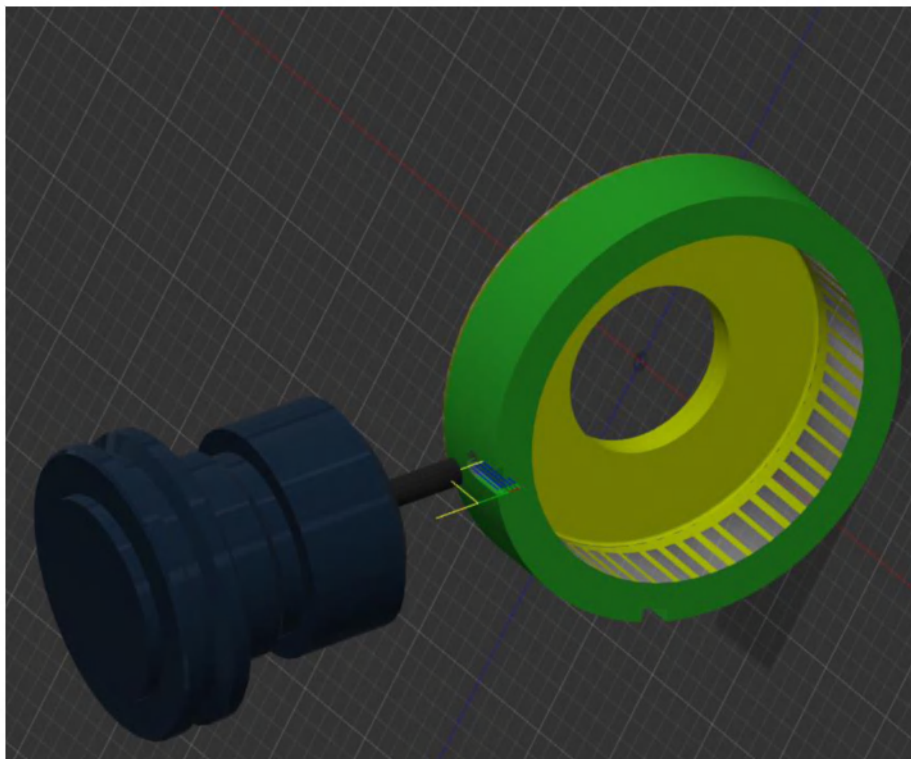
Операція 9. Виготовлення пазів для ключа під круглi гайки
